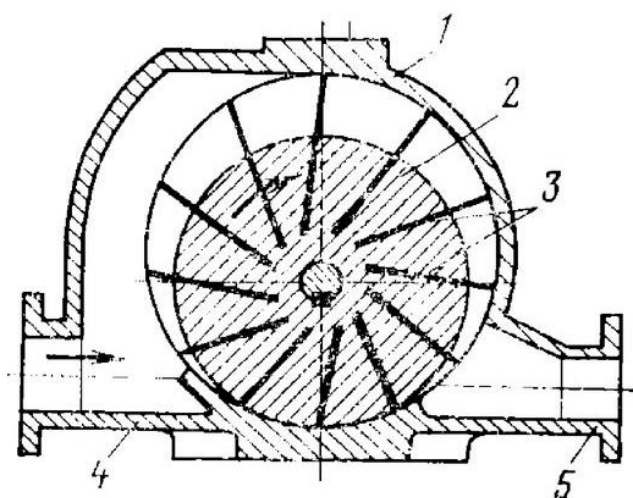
Одноступенчатый пластинчатый компрессор:
